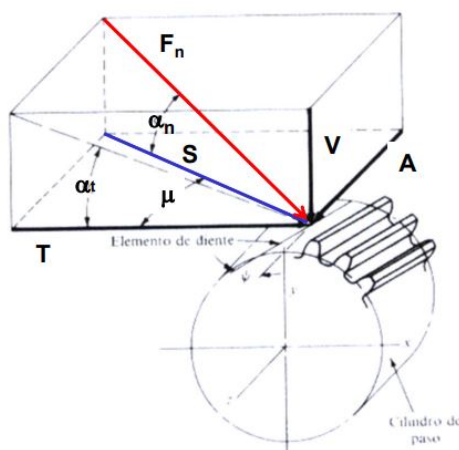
Cargas generadas en la transmisión con engranajes cilíndricos helicoidales.
